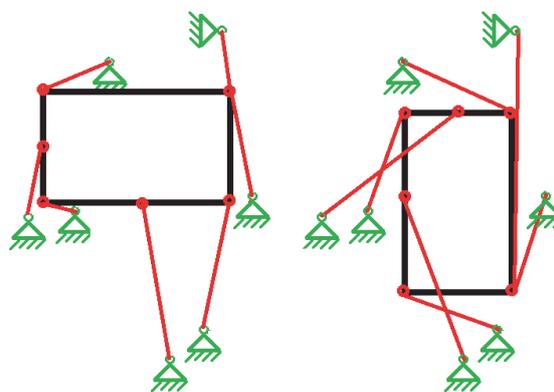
Расчетная схема для определения угла поворота стола вокруг вертикальной оси
